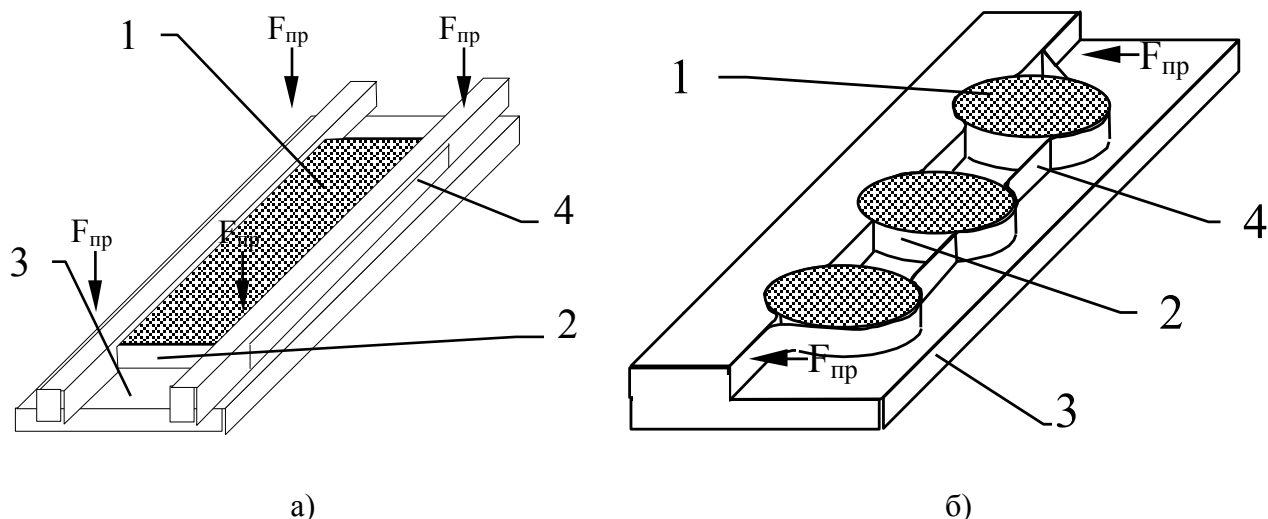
Варіанти затискних пристосувань для затиску оптичних виробів прямокутної (а) та круглої (б) форми: $F_{пр}$ – притискаюча сила; 1 – поверхня, яка підлягає обробці; 2 – заготівка; 3 – основа; 4 – базуючі поверхні; 5 – фіксуюча стрічка
